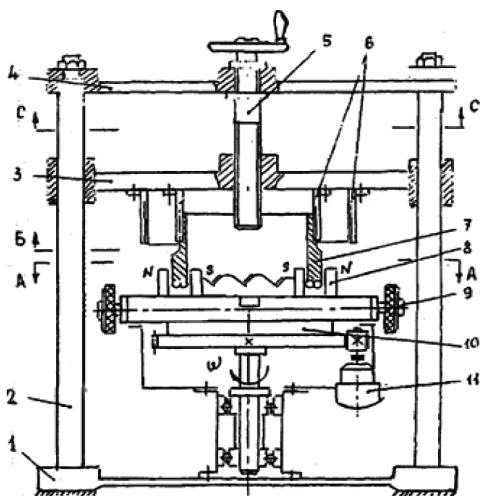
Стенд для обработки коронок вращающимся магнитным полем: 1 — опорная плита; 2 — направляющие; 3 — подвижная траверса; 4 — неподвижная траверса с винтом; 5 — винт подачи коронок; 6 — втулки с резьбой для установки коронок на стенде; 7 — буровая коронка; 8 — магниты; 9 — винт перемещения магнитов под коронки разных диаметров; 10 — вращающийся стол; 11 — привод стола
